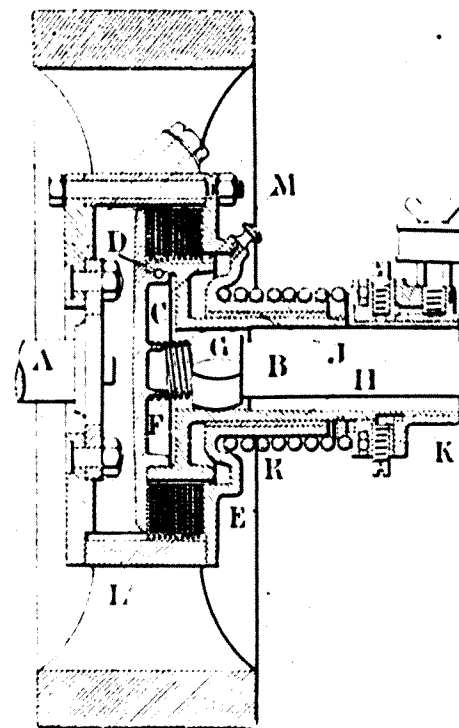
Embrayage à disques, à tambour central mobile type Ariès.
